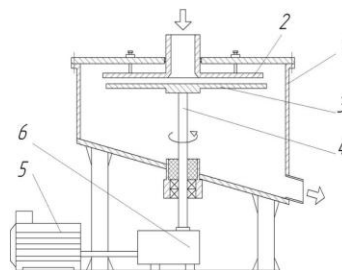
Схема млина: 1 - корпус; 2 – нерухомий диск; 3 – рухомий диск; 4 – вал; 5 - електродвигун; 6 – редуктор
